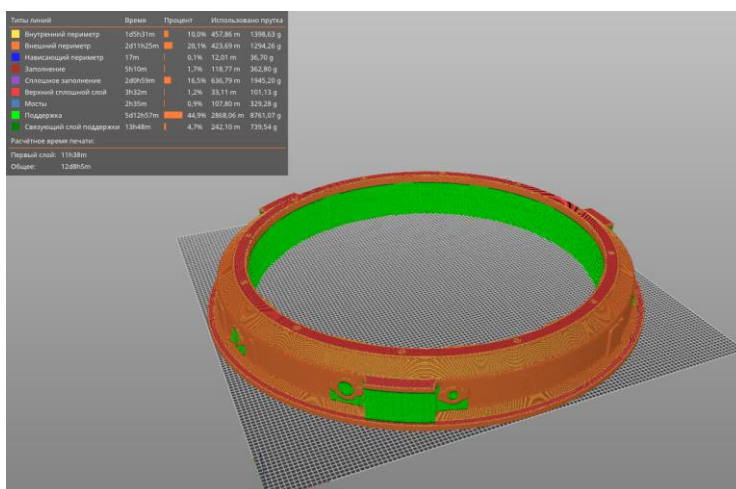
Процесс слайсинга 3D модели отливки детали
